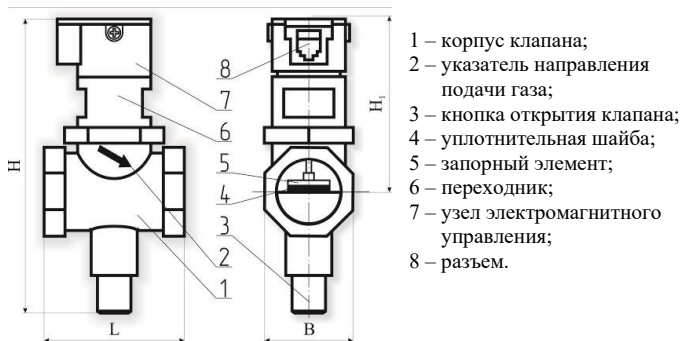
Внешний вид клапанов КЗЭУГ
